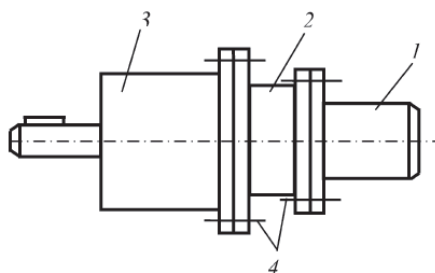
Компонировка мотор-вариатора-редуктора
